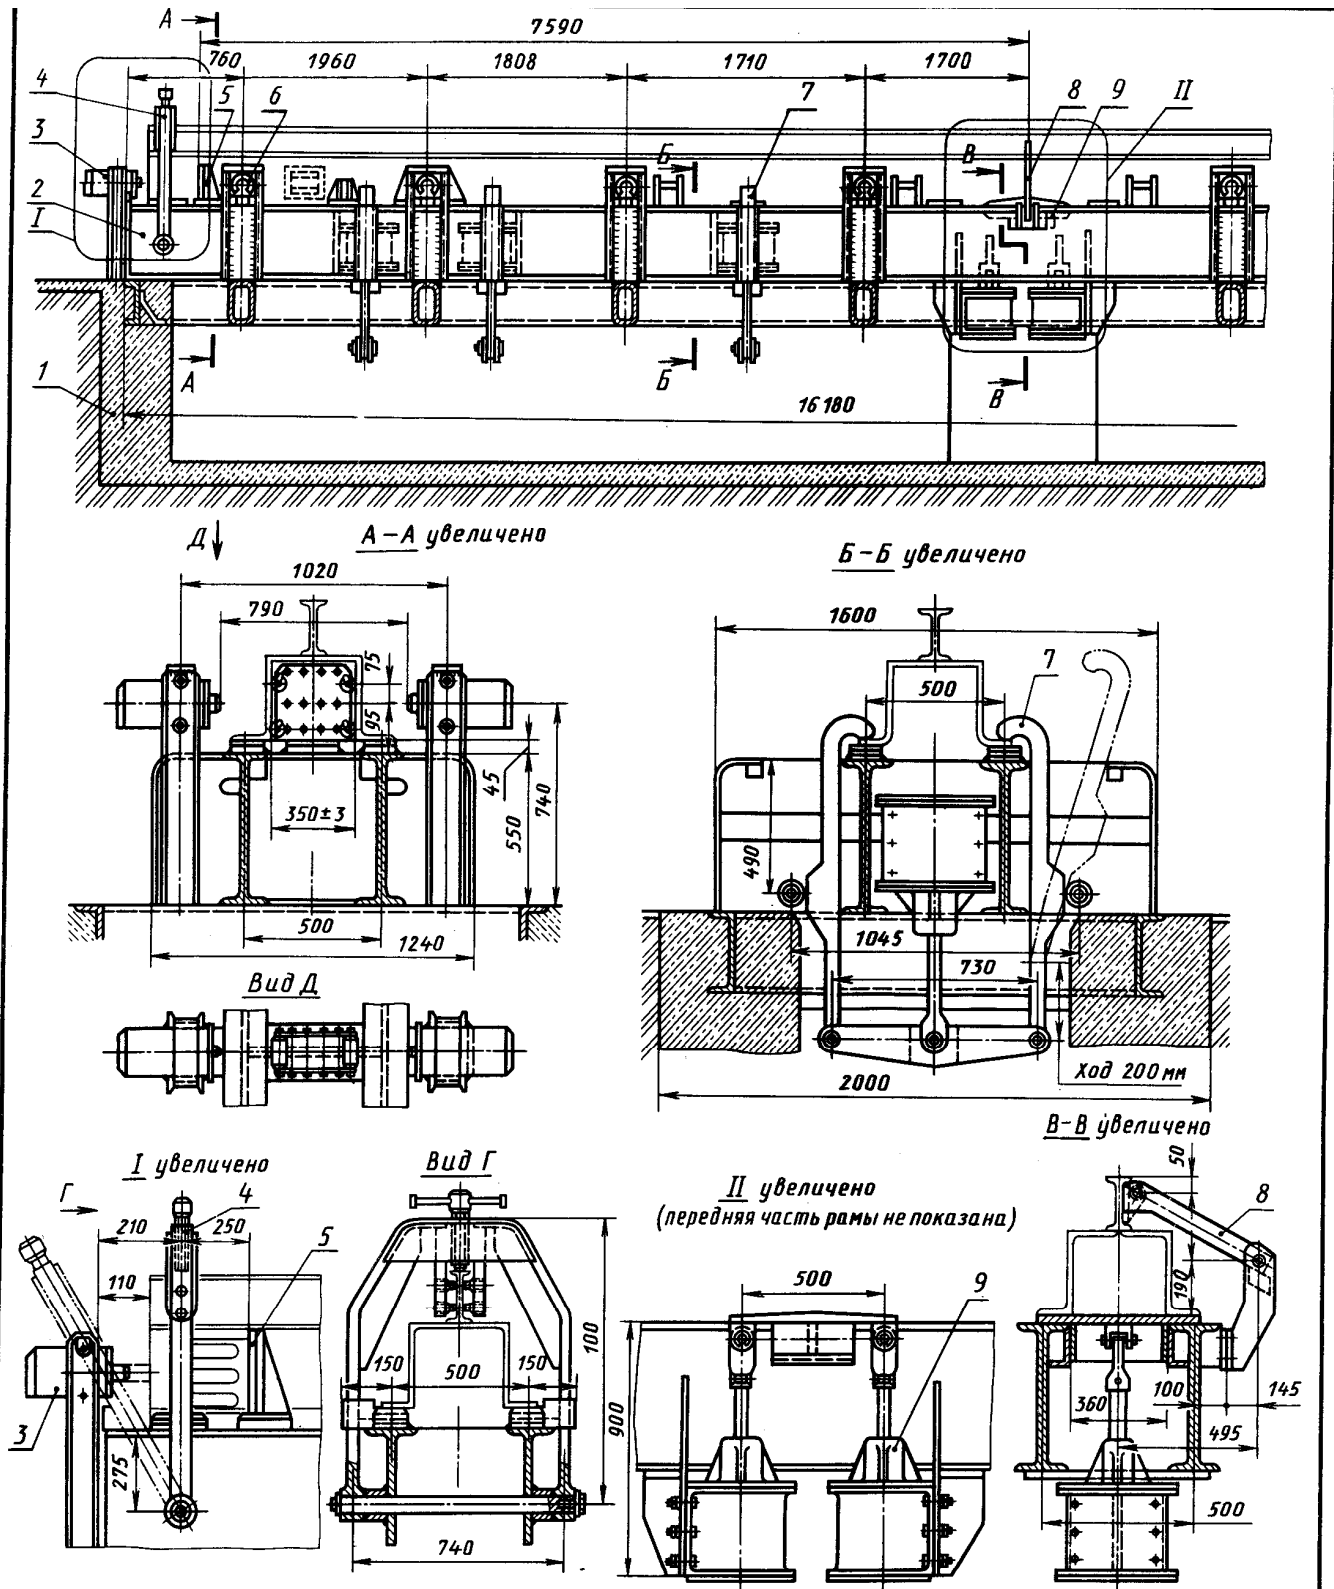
Приспособление для сборки и сварки хребтовых балок полувагона
